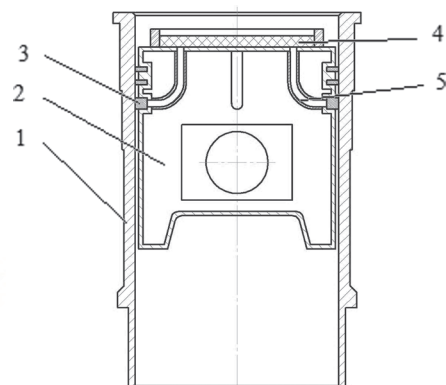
Схема смазывания рабочей поверхности гильзы цилиндра
